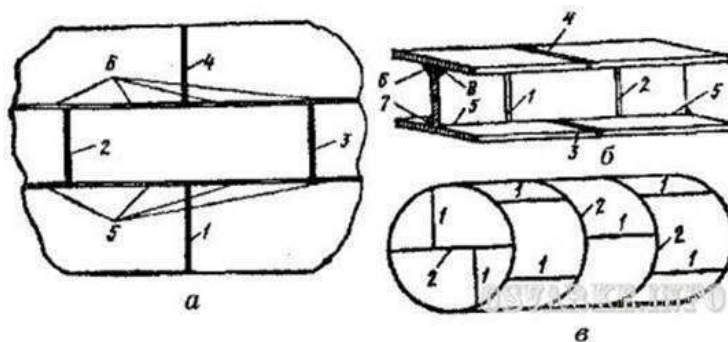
Последовательность наложения швов (1-8) при сварке:
